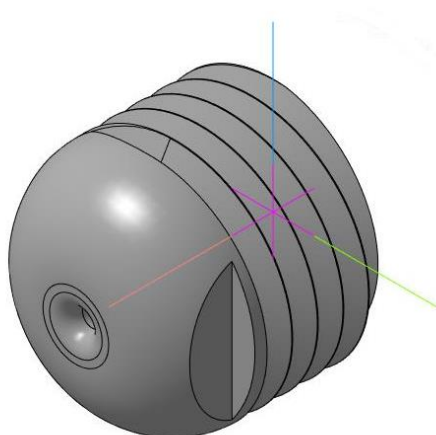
Фиксатор крепления заднего корпуса. 3D модель
